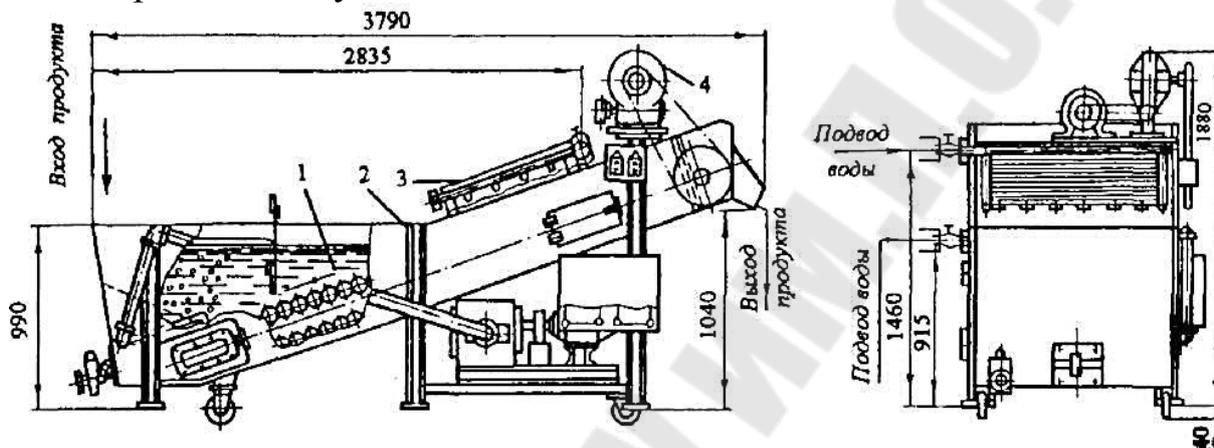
Линейная моечная машина элеваторного типа: 1 - ванна; 2 - транспортерное полотно; 3 - душевое устройство; 4 - привод
